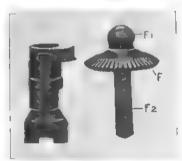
Achse mit Kegelrad u. Kugelgelenk; links: Pumpenexcenter und Cardangelenk.
